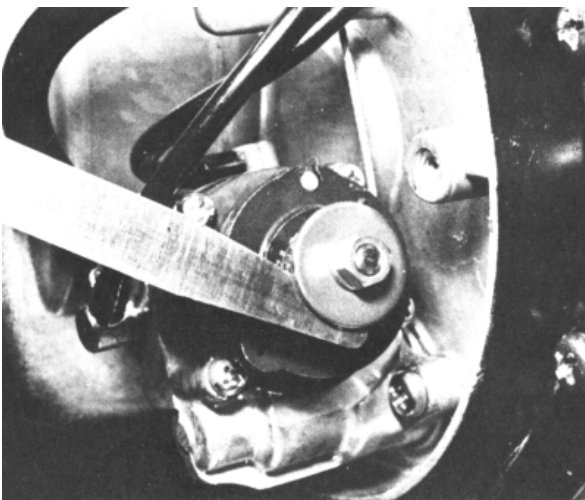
Den Pumpenhub mit der Fühlerblattelehre messen
